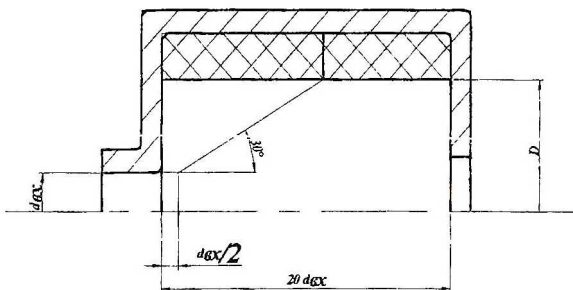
Конструктивная схема цилиндрического глушителя шума.
